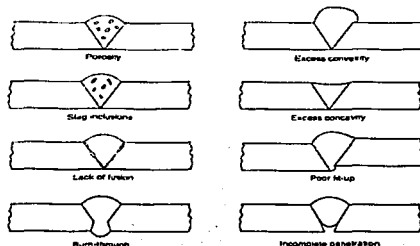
Esquema de algunos defectos típicos en soldadura [11].
